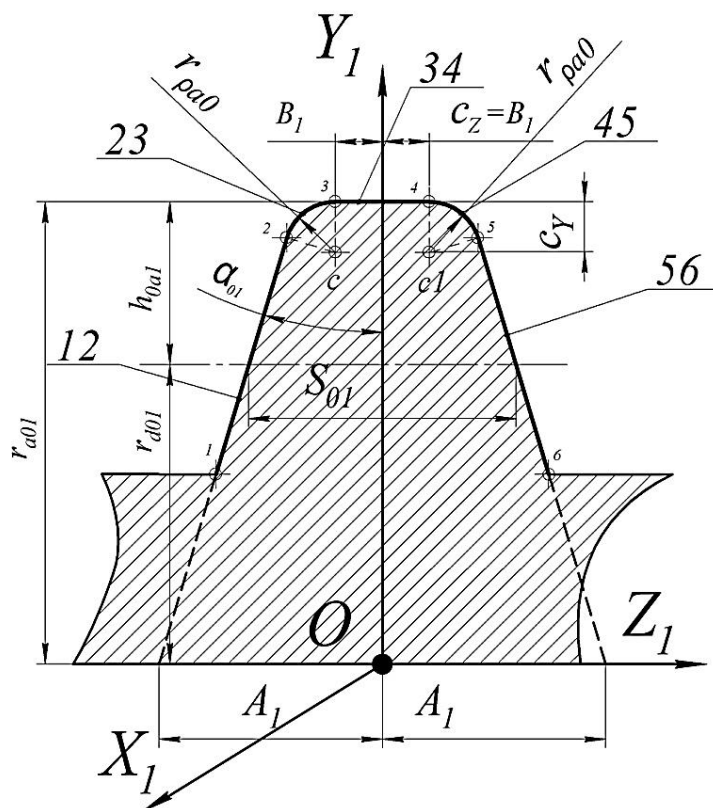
Твірний профіль вихідної інструментальної поверхні стандартної черв'ячної фрези
